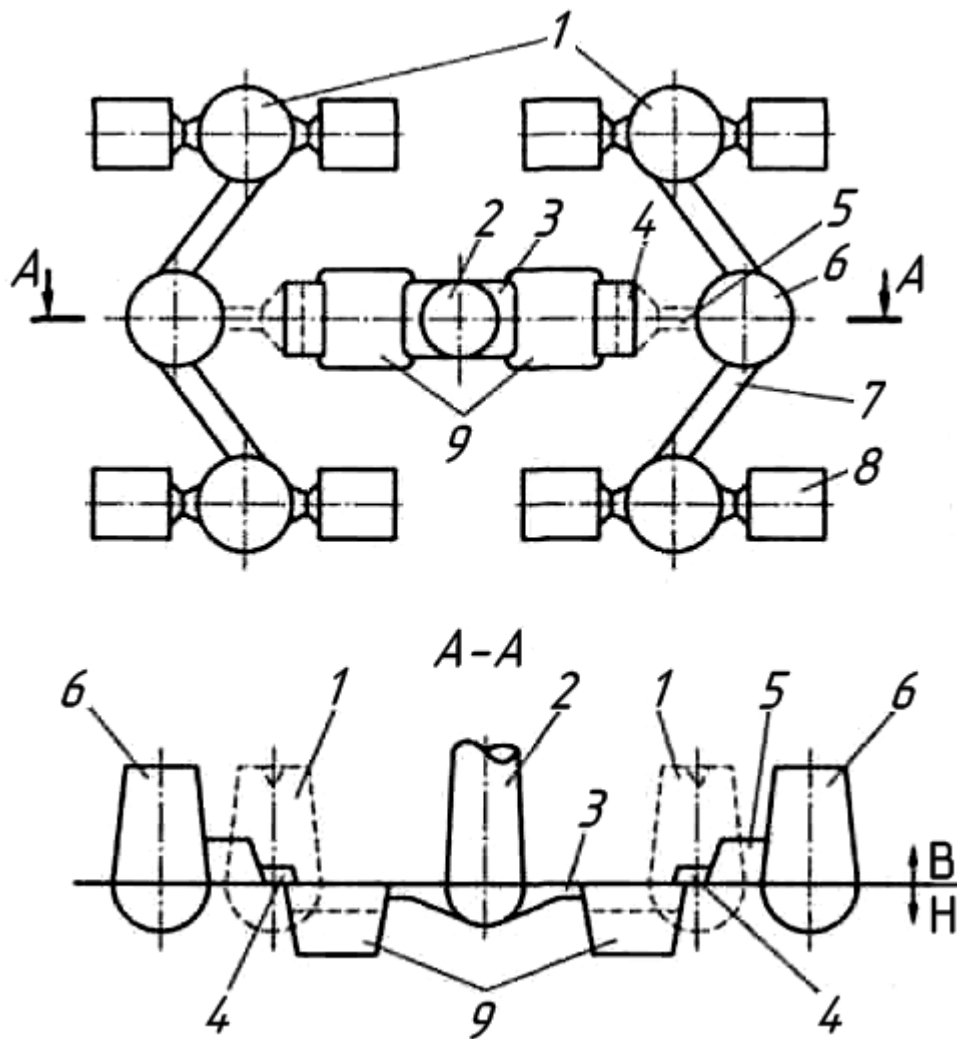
Пример литниковой системы с несколькими отливками в опоке
